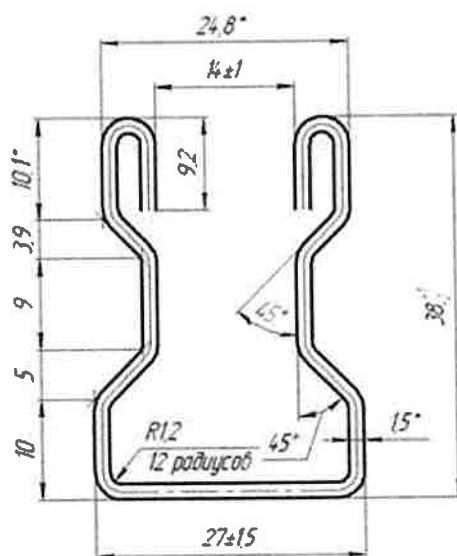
Профиль U-образный (размер заготовки 122,5 мм)
